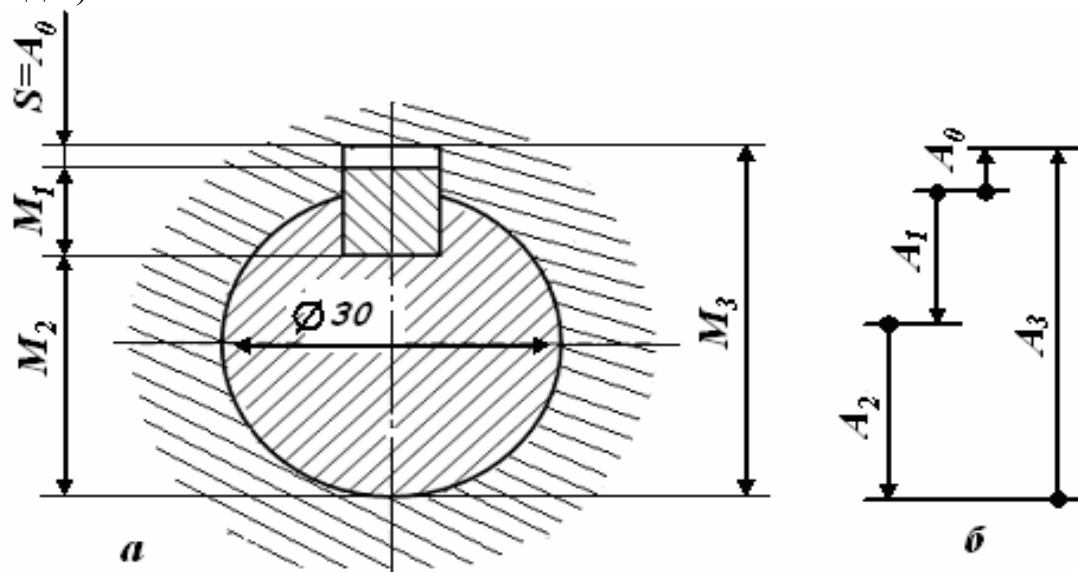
Шпонкове з'єднання: а – складальний кресленик; б – геометрична схема розмірного ланцюга
